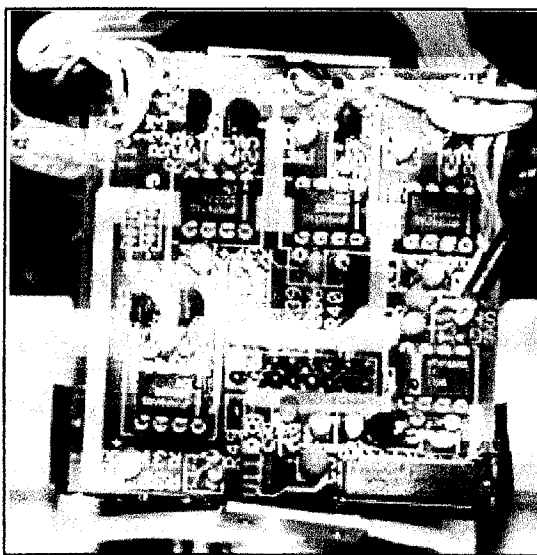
Placa de pré- amplificação, vista pelo lado dos componentes.
